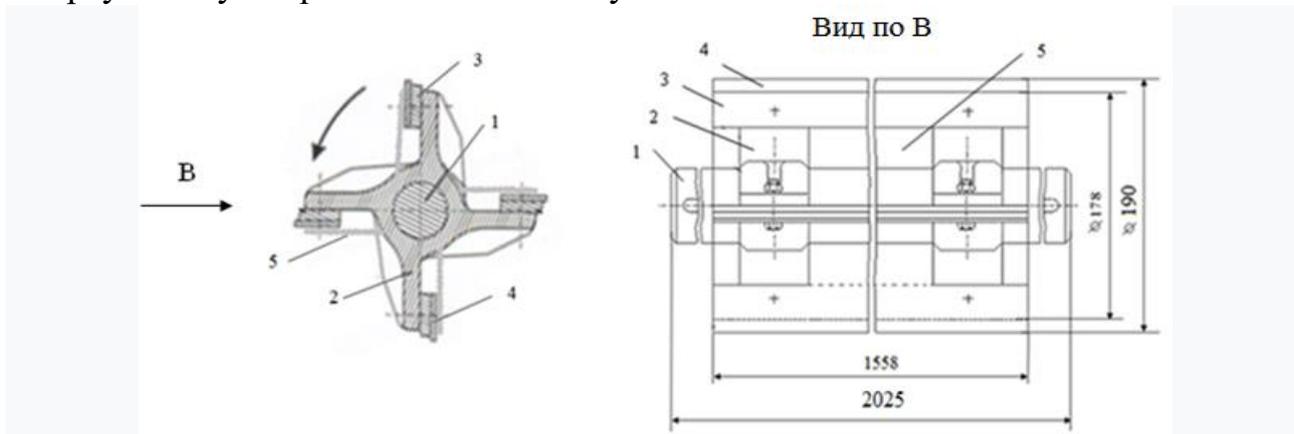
Сборочный чертеж ворошителя модернизированной конструкции
